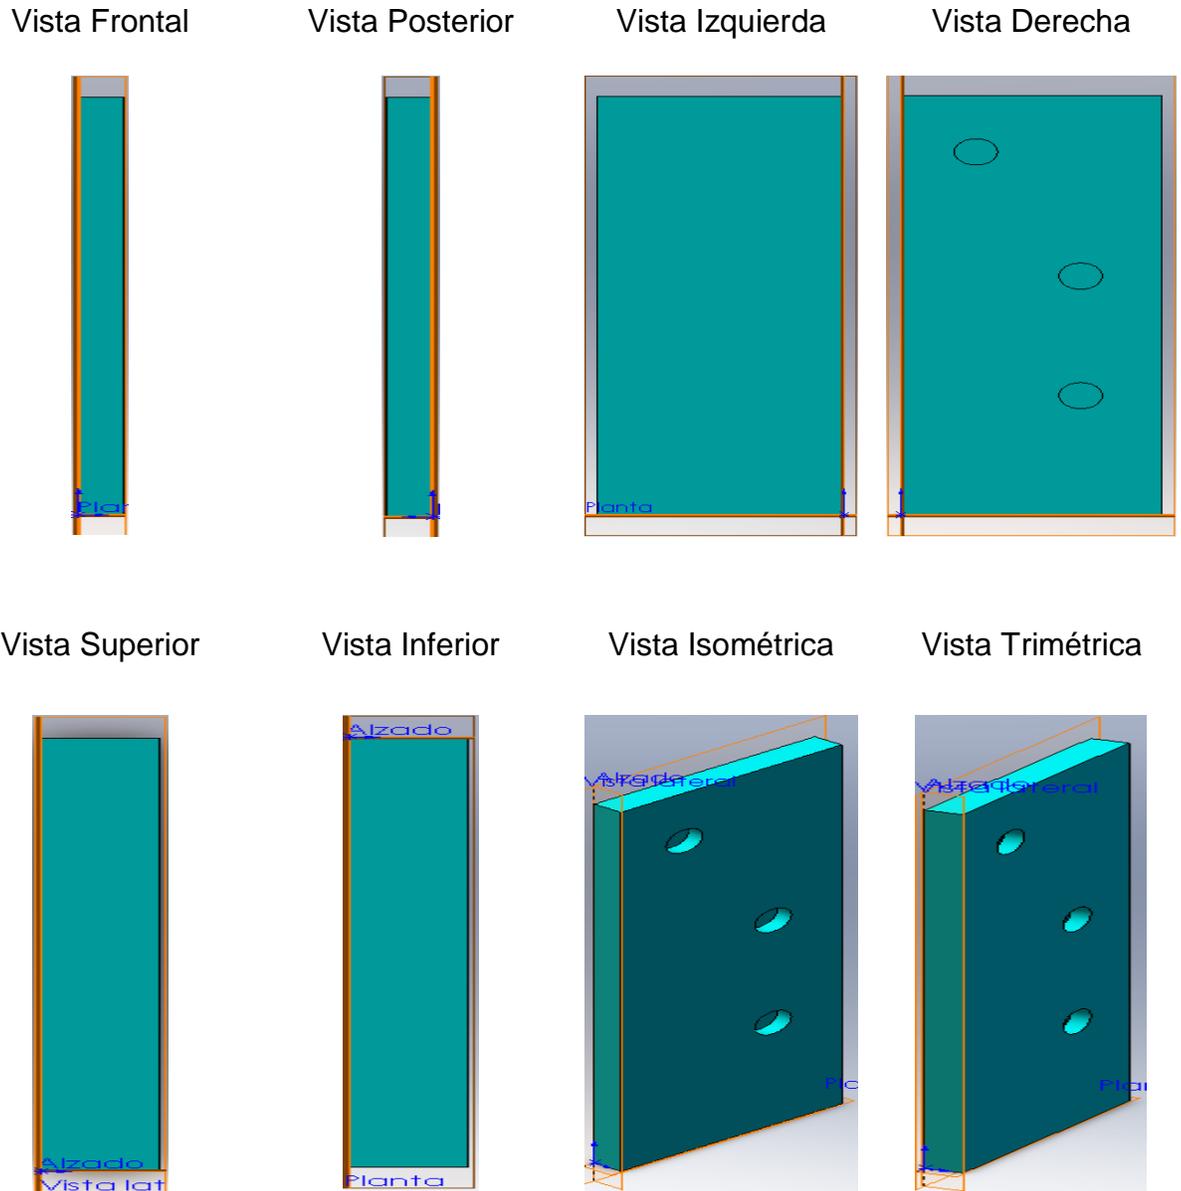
Vistas de la placa izquierda sujetadora de los rodillos tensores frontales.
